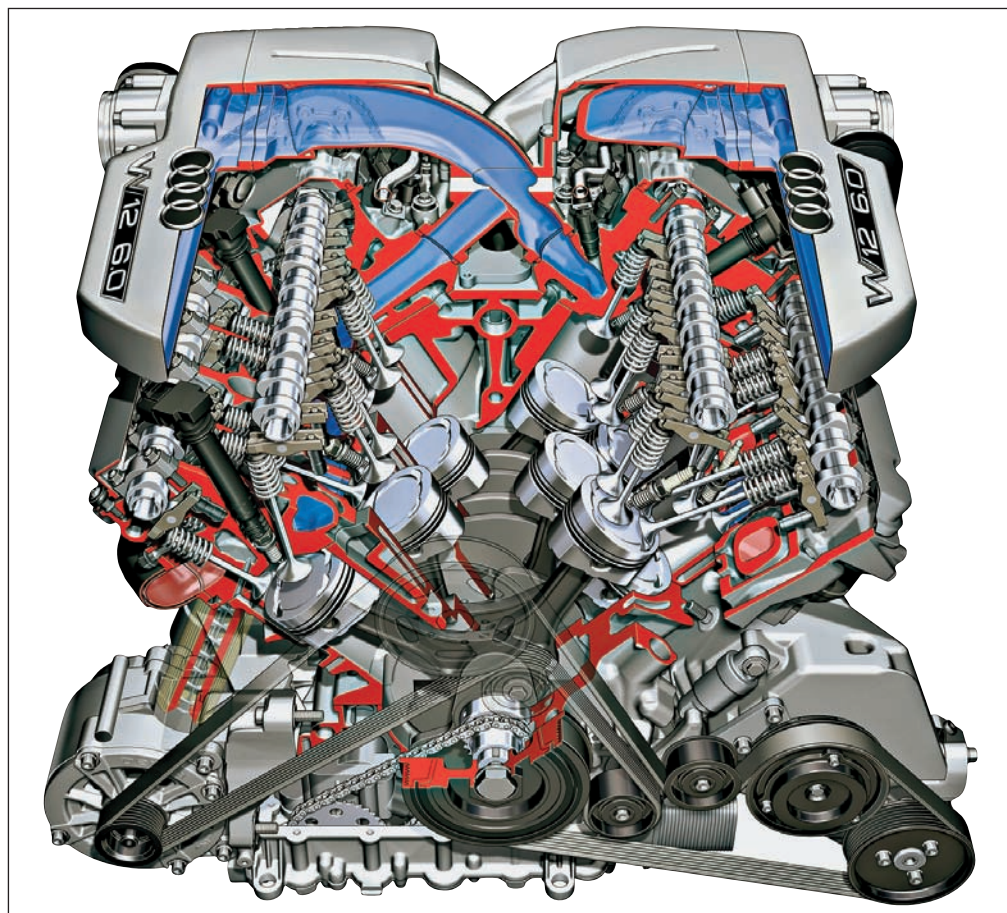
Двигатель W12, устанавливаемый на Audi A8 с 2001 г., практически состоит из двух двигателей V6 с различными углами развала цилиндров, использующих общий коленчатый вал
